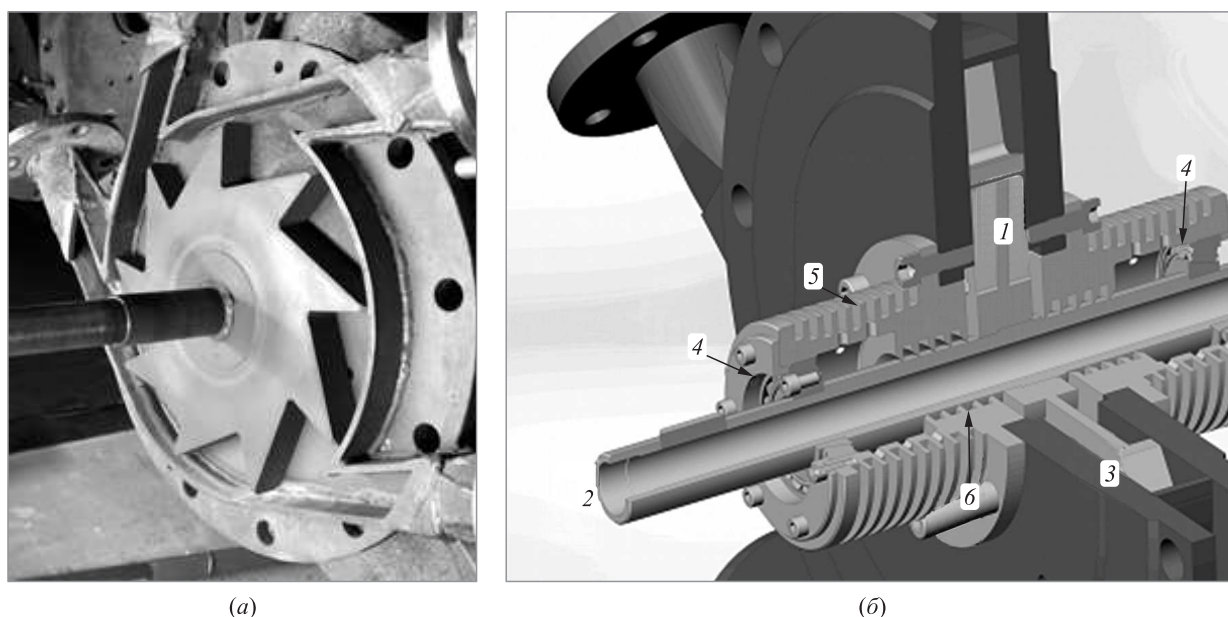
Экспериментальный образец импульсной турбины: (а) фотография; (б) крепление ротора (1 — ротор с лопатками; 2 — вал; 3 — корпус; 4 — подшипники; 5 — обойма с ребрами охлаждения; 6 — уплотнения)
